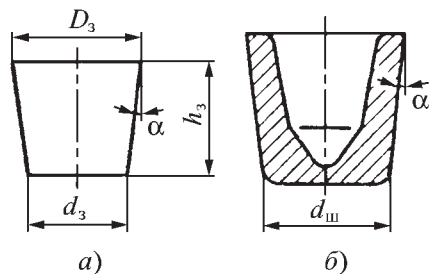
Переходы штамповки типа стакана с глубокой полостью
